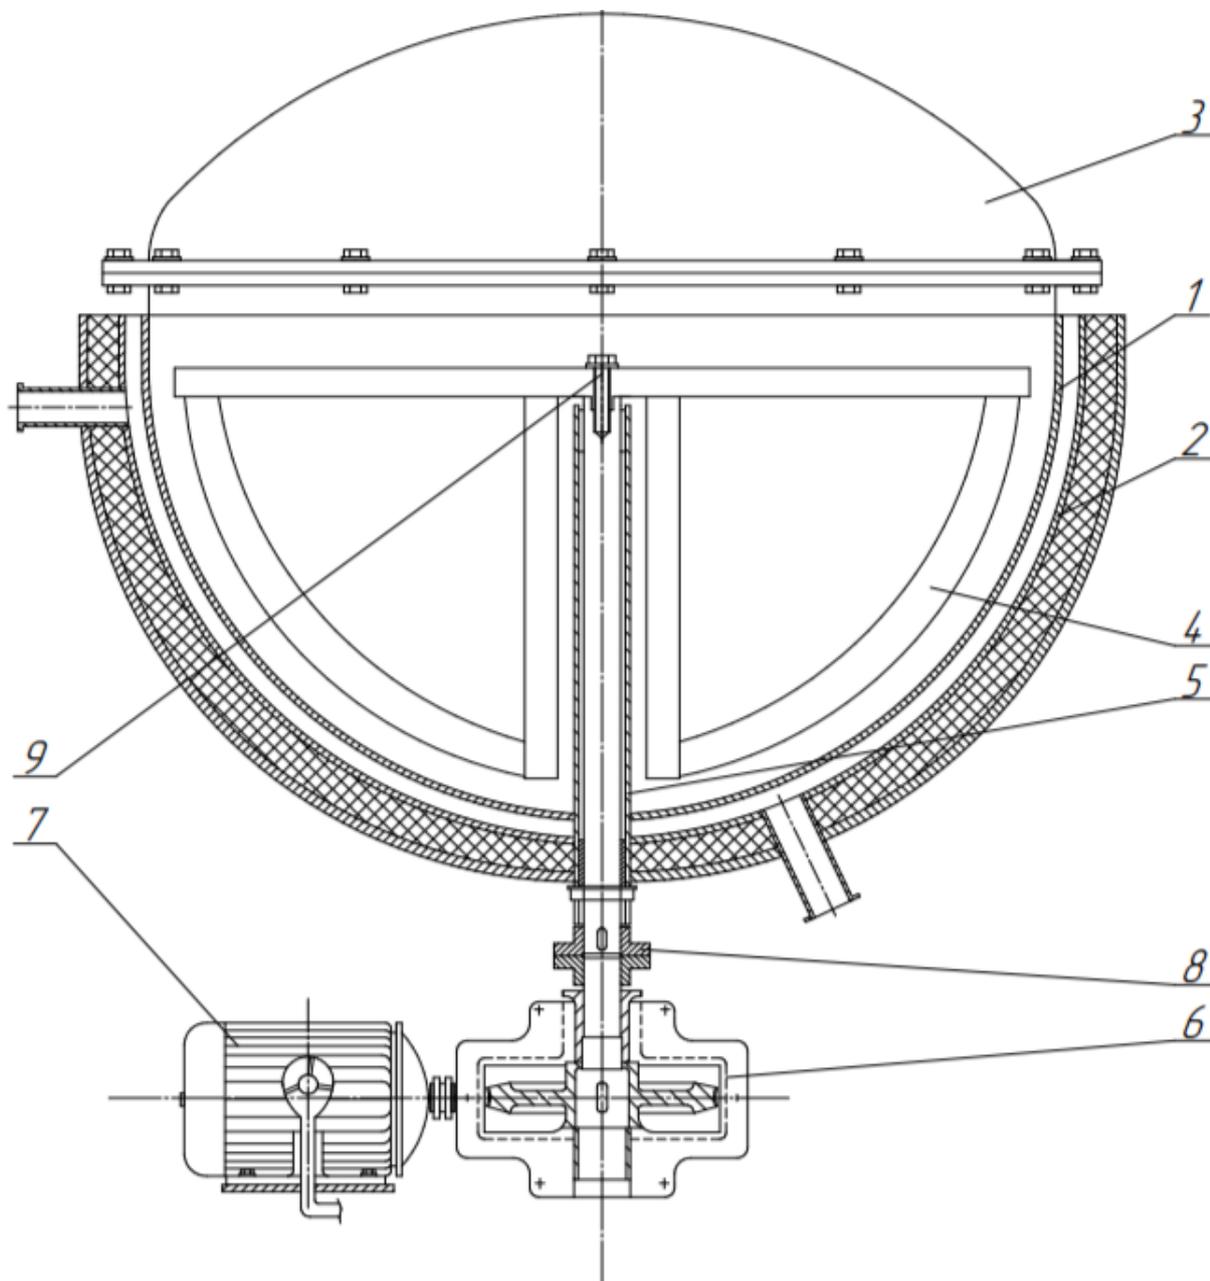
Конструктивная схема узла варочный сосуд-рубашка-перемешивающее устройство
